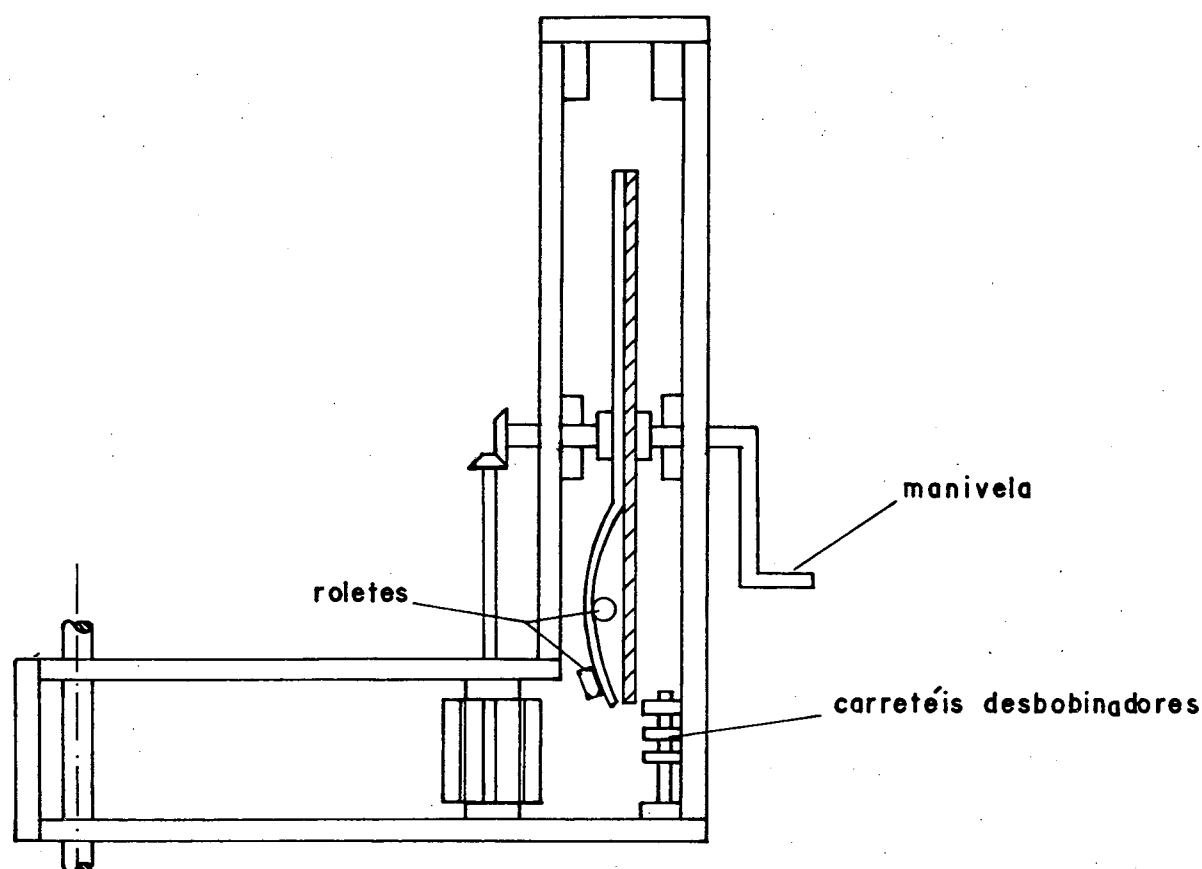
Vista superior dos conjuntos alimentador e plantador.
